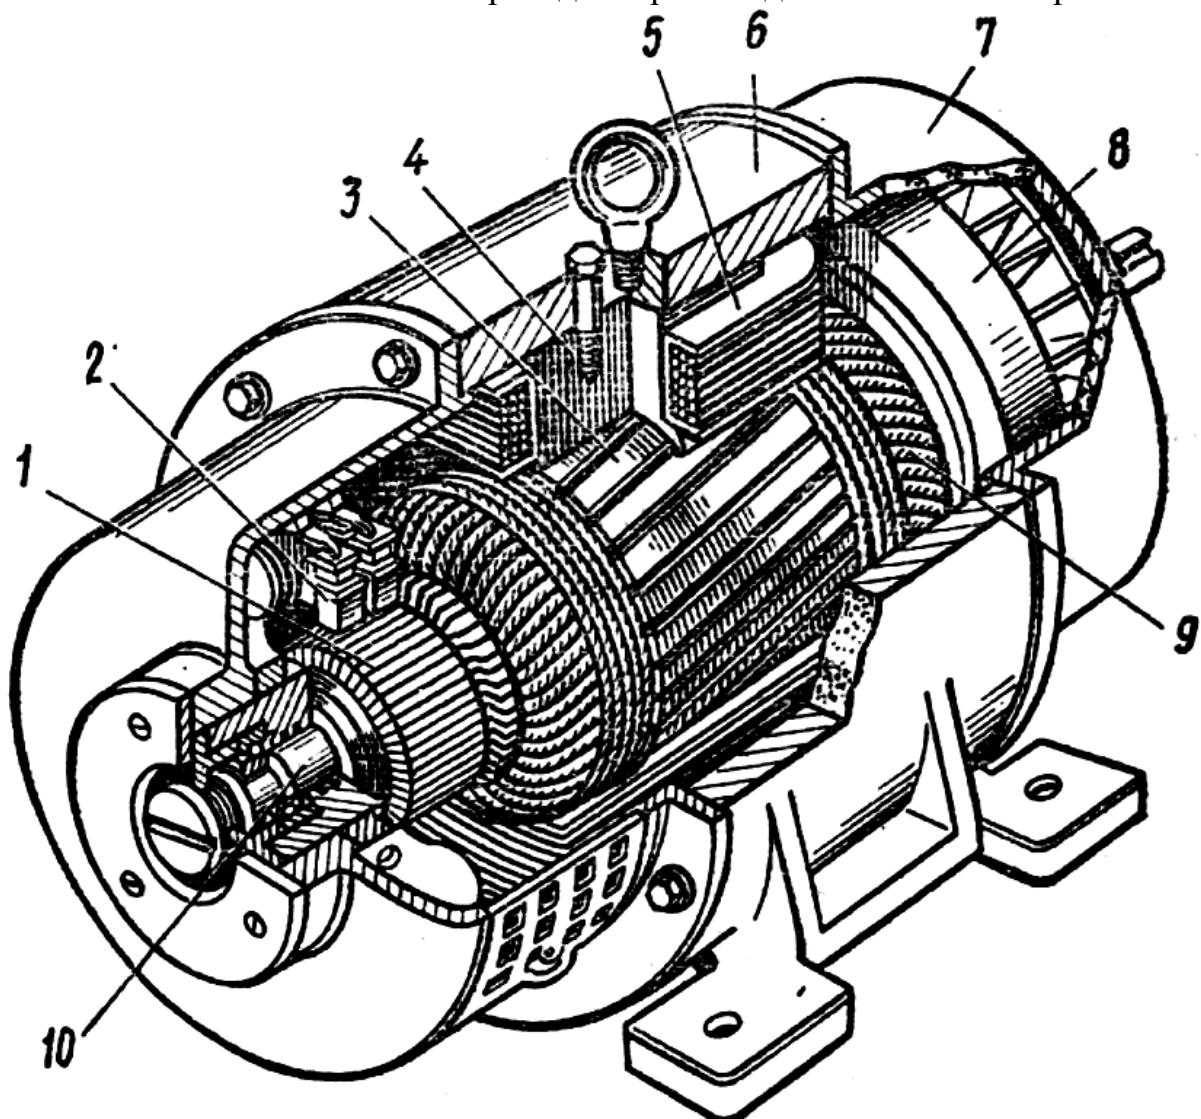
Устройство электрической машины постоянного тока: 1 – коллектор; 2 – щетки; 3, 9 – сердечник и обмотка якоря; 4 – главный полюс; 5 – катушка обмотки возбуждения; 6 – станина (корпус); 7 – подшипниковый щит; 8 – вентилятор; 10 – вал.
